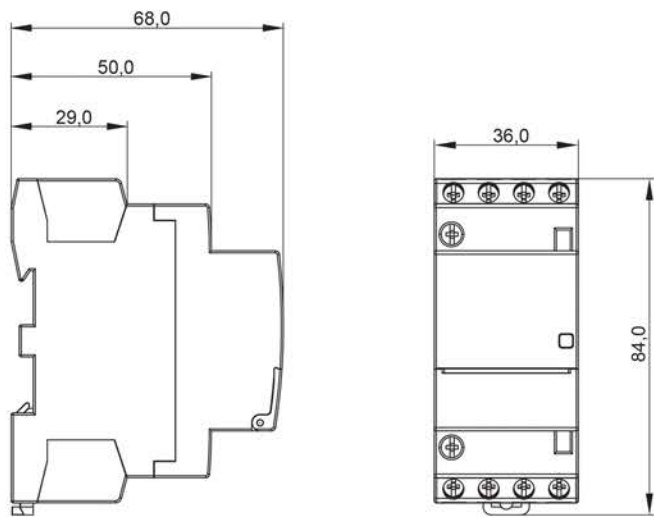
Габаритные размеры контакторов до 25 А, 4P / Figure 2 – Overall dimensions of contactors up to 25 A, 4P
